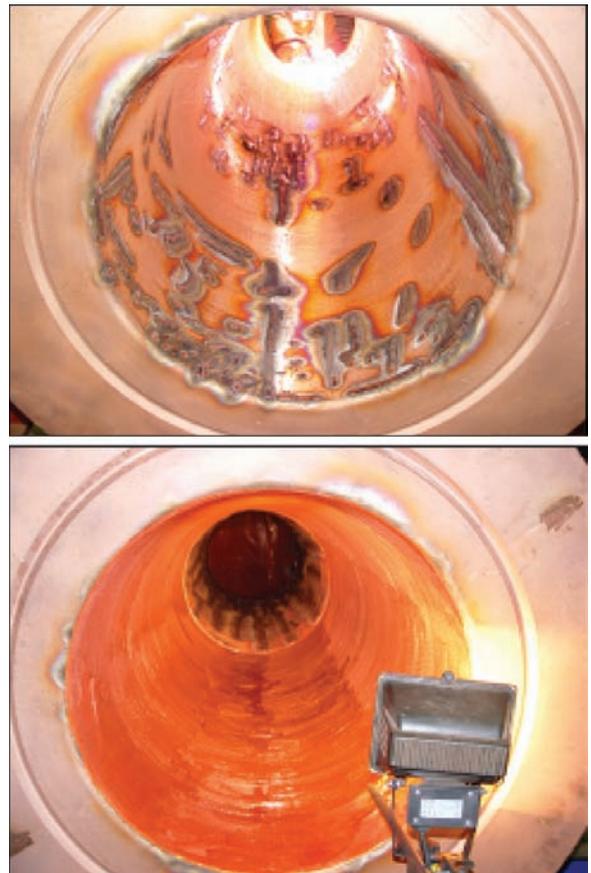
Ремонт поверхности кокилей точечной сваркой
